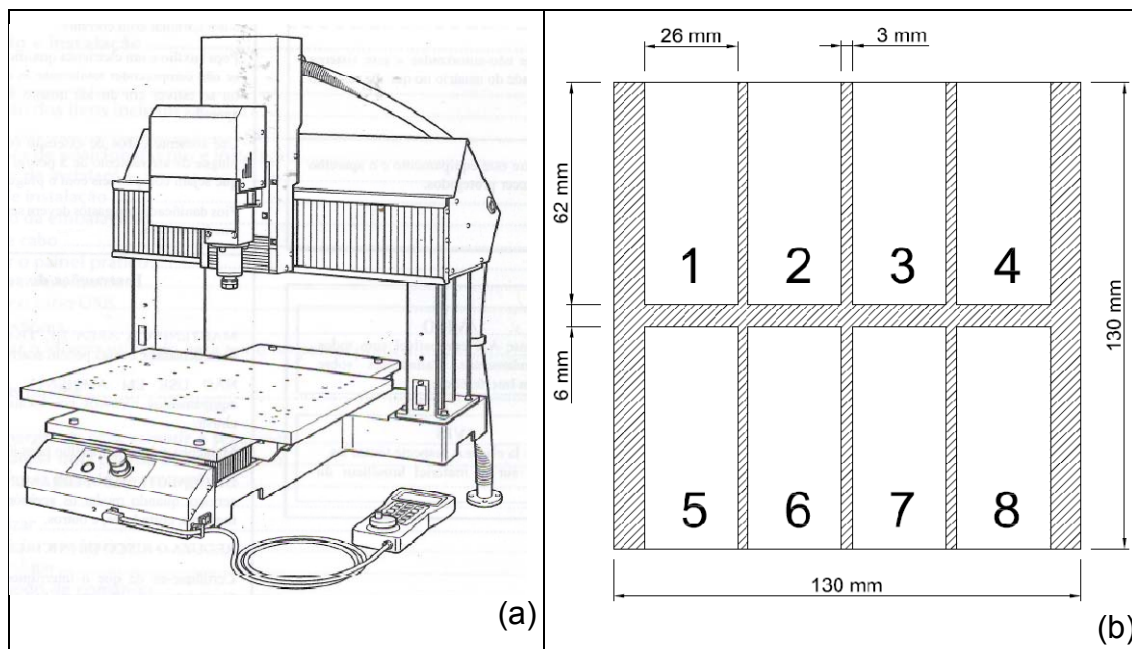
(a) Fresa automática Roland Modelo MDX-540 e (b) esquema de usinagem para obtenção dos corpos de prova de EWF.
